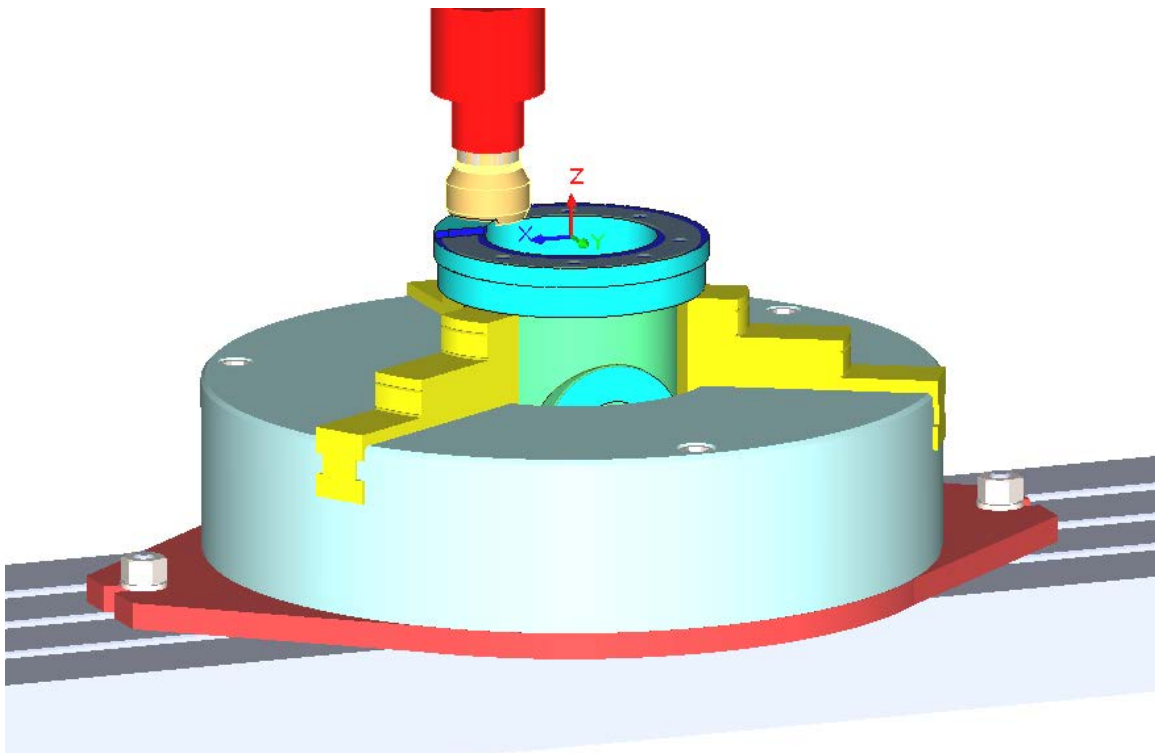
Фрагмент імітації обробки комплекту поверхонь 1- фрезерування торцевою фрезою.
